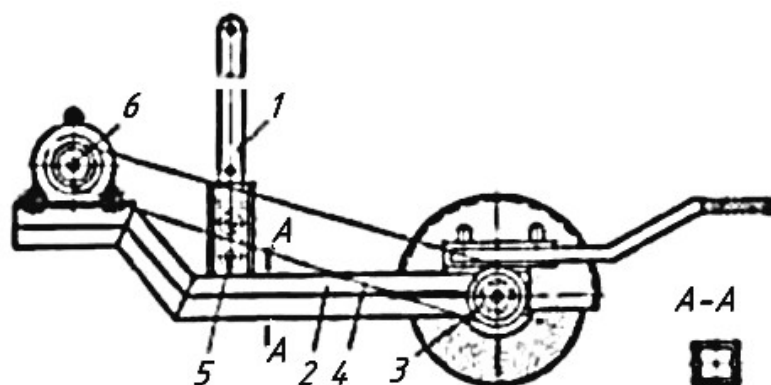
Подвесной обдирочный станок: 1 — подвеска; 2 — рама; 3 — шкив; 4 — ремень; 5 — шарнир; 6 — электродвигатель
